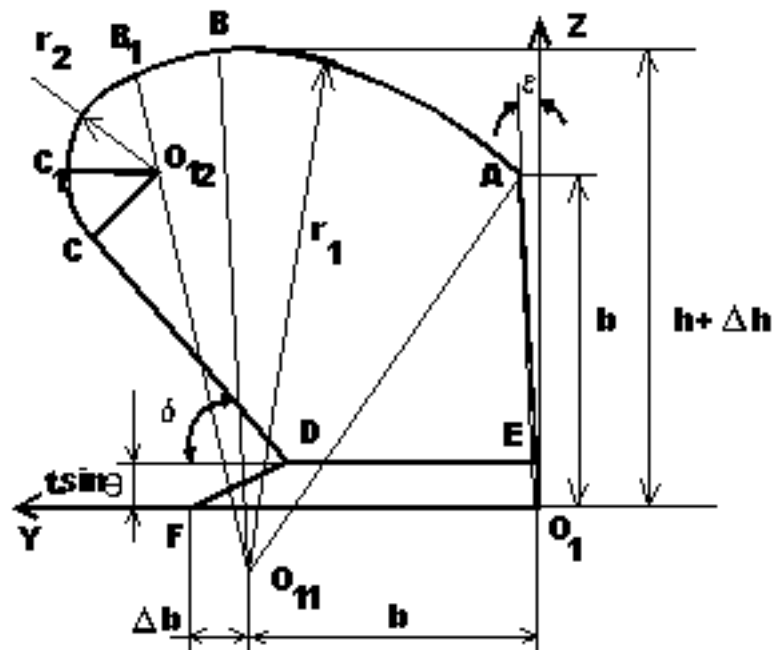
Dimensions principales d'un corps de charrue vue de face
